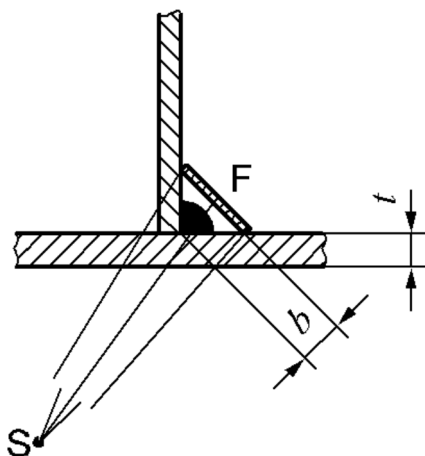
Схема контроля при просвечивании угловых сварных швов
